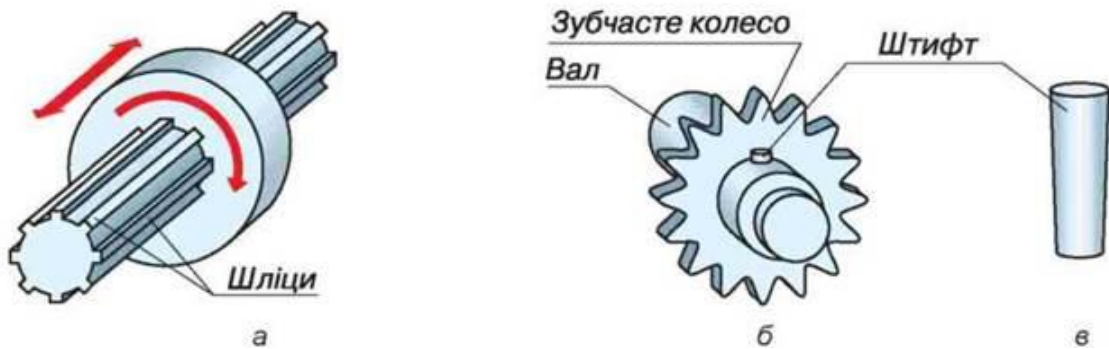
З'єднання: а - шліцьове; б - штифтове; в - штифт
